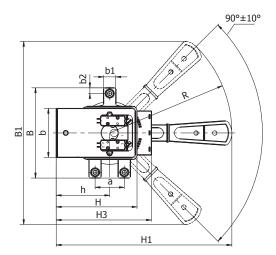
Выключатель-разъединитель трехполюсный на два направления с боковой смещенной рукояткой.
